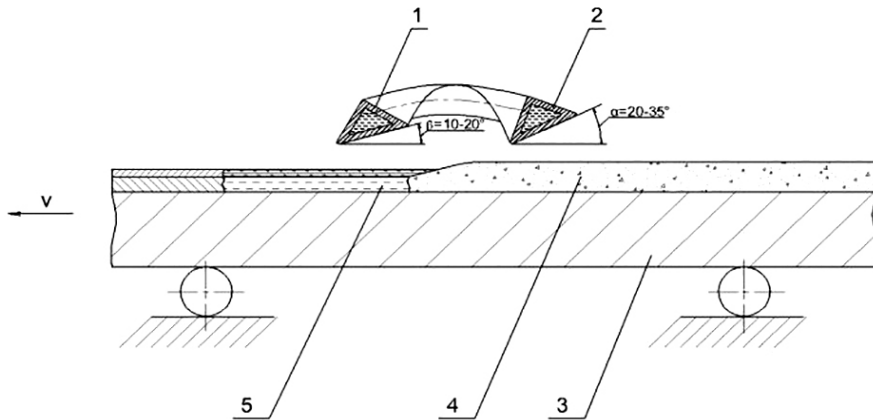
Индуктор для автоматической односторонней наплавки и схема осуществления 2-зонной наплавки
